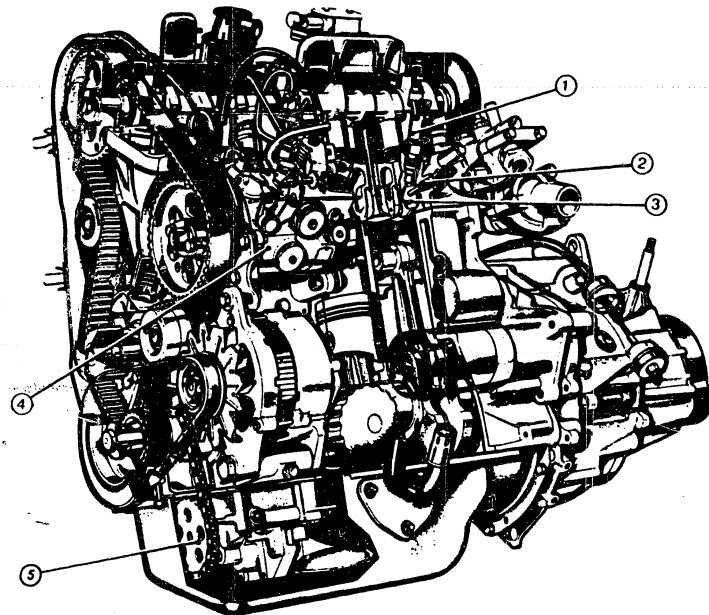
Der BX-19 Dieselmotor teilweise geschnitten. Es bedeuten:
